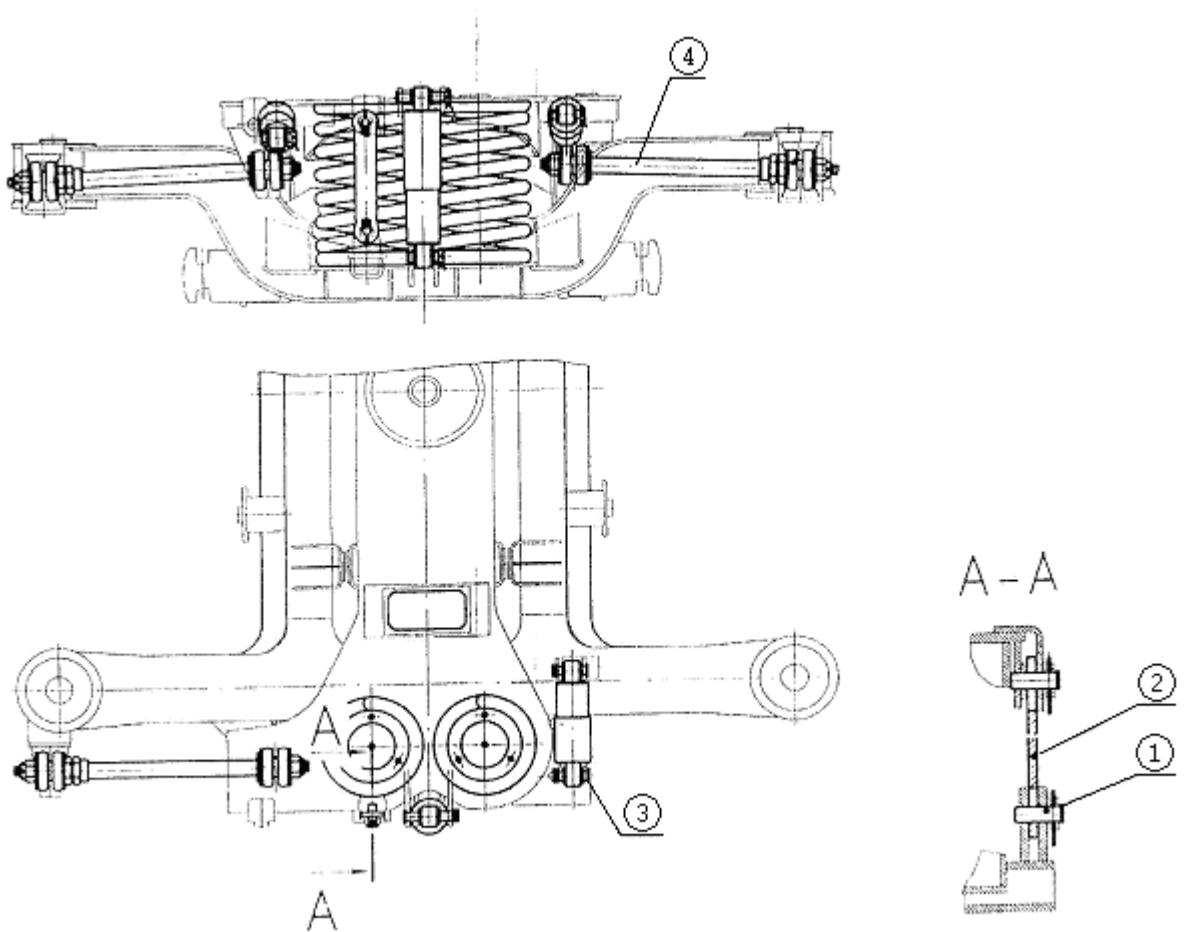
Дефекты узлов и деталей центрального подвешивания безлюлечных тележек моделей 68-4095, 68-4096, 68-4075 и 68-4076, ремонтируемые сваркой или наплавкой
